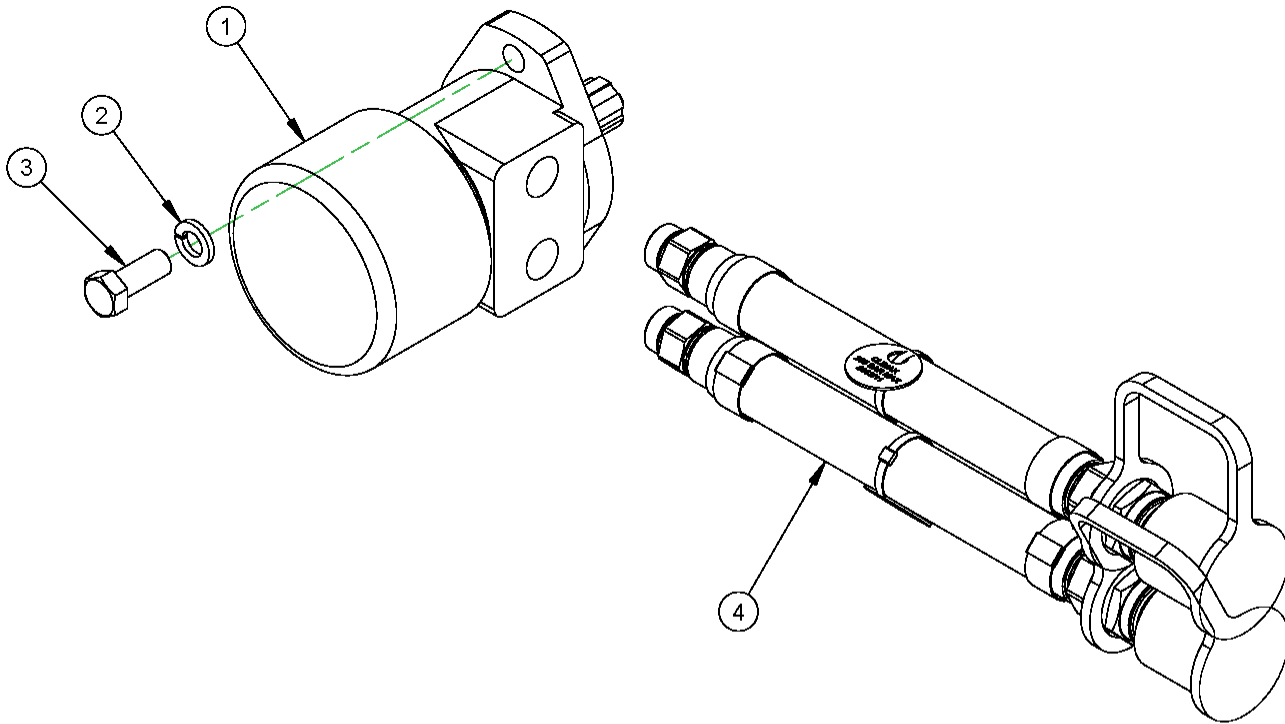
Ensemble bras coulissant de barre d'alésage (Réf. 72875)
